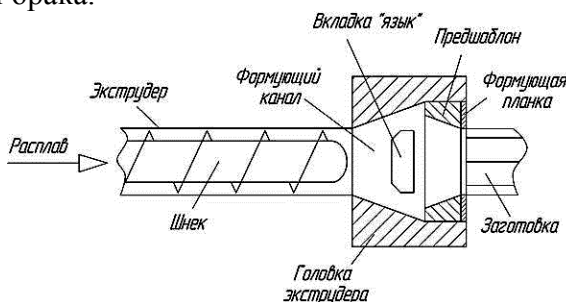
Схематичное изображение канала течения резиновой смеси (вид сверху)
